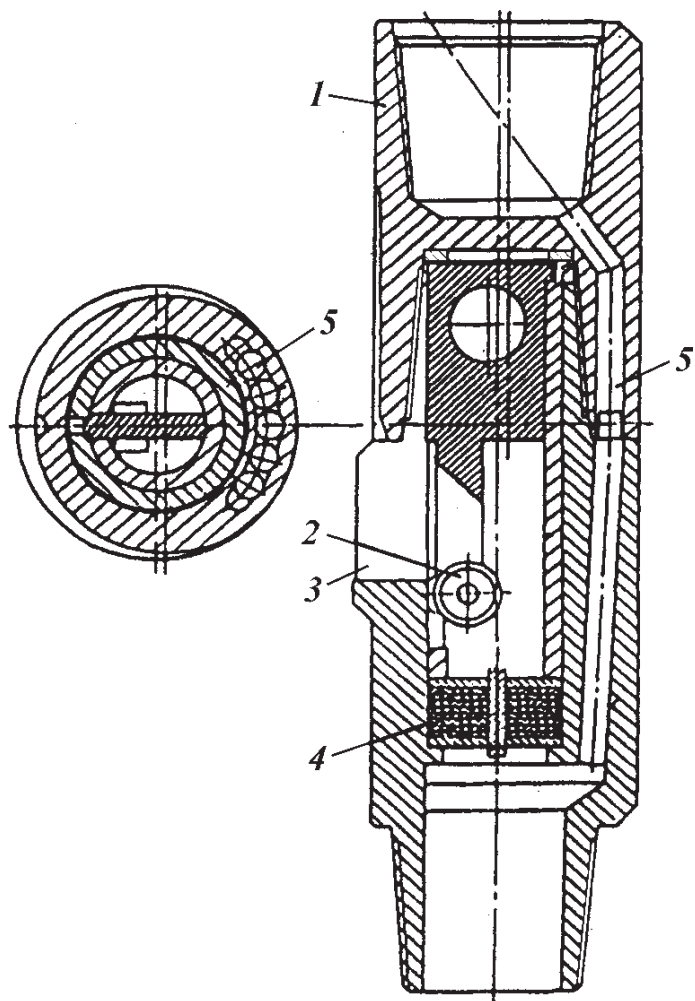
Приспособление для передвижения каротажных приборов:
